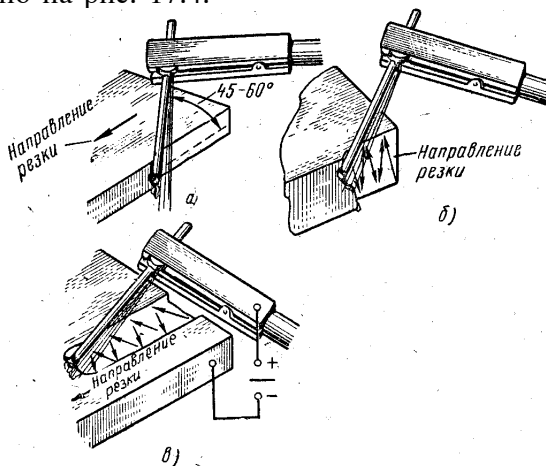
Положение резака при воздушно-дуговой резке:
